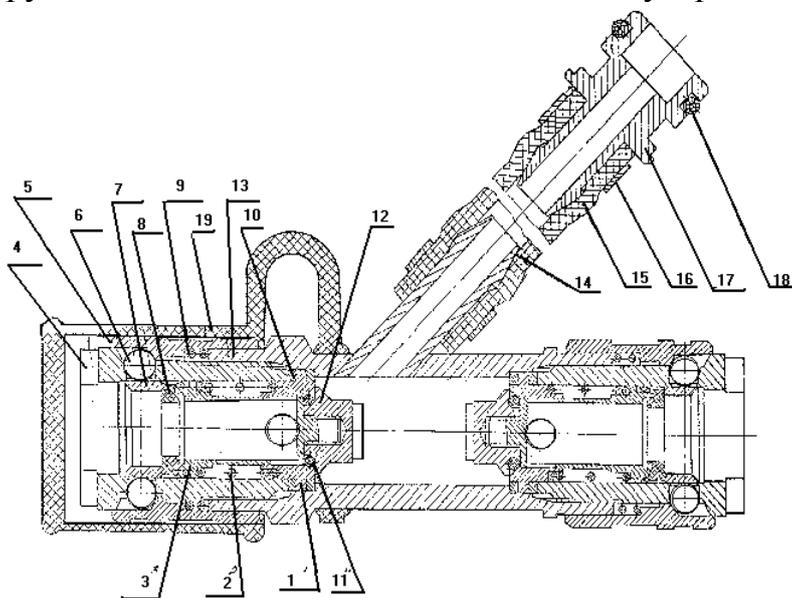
Разъем: 1 – седло; 2 – пружина; 3, 4 – корпус; 5 – обойма; 6 – шарики; 7 – втулка; 8 – манжета; 9 – пружина; 10 – кольцо; 11 – уплотнительное кольцо; 12 – клапан; 13 – корпус; 14,17 – штуцер; 15 – шланг; 16 – кольцо; 18 – уплотнительное кольцо
